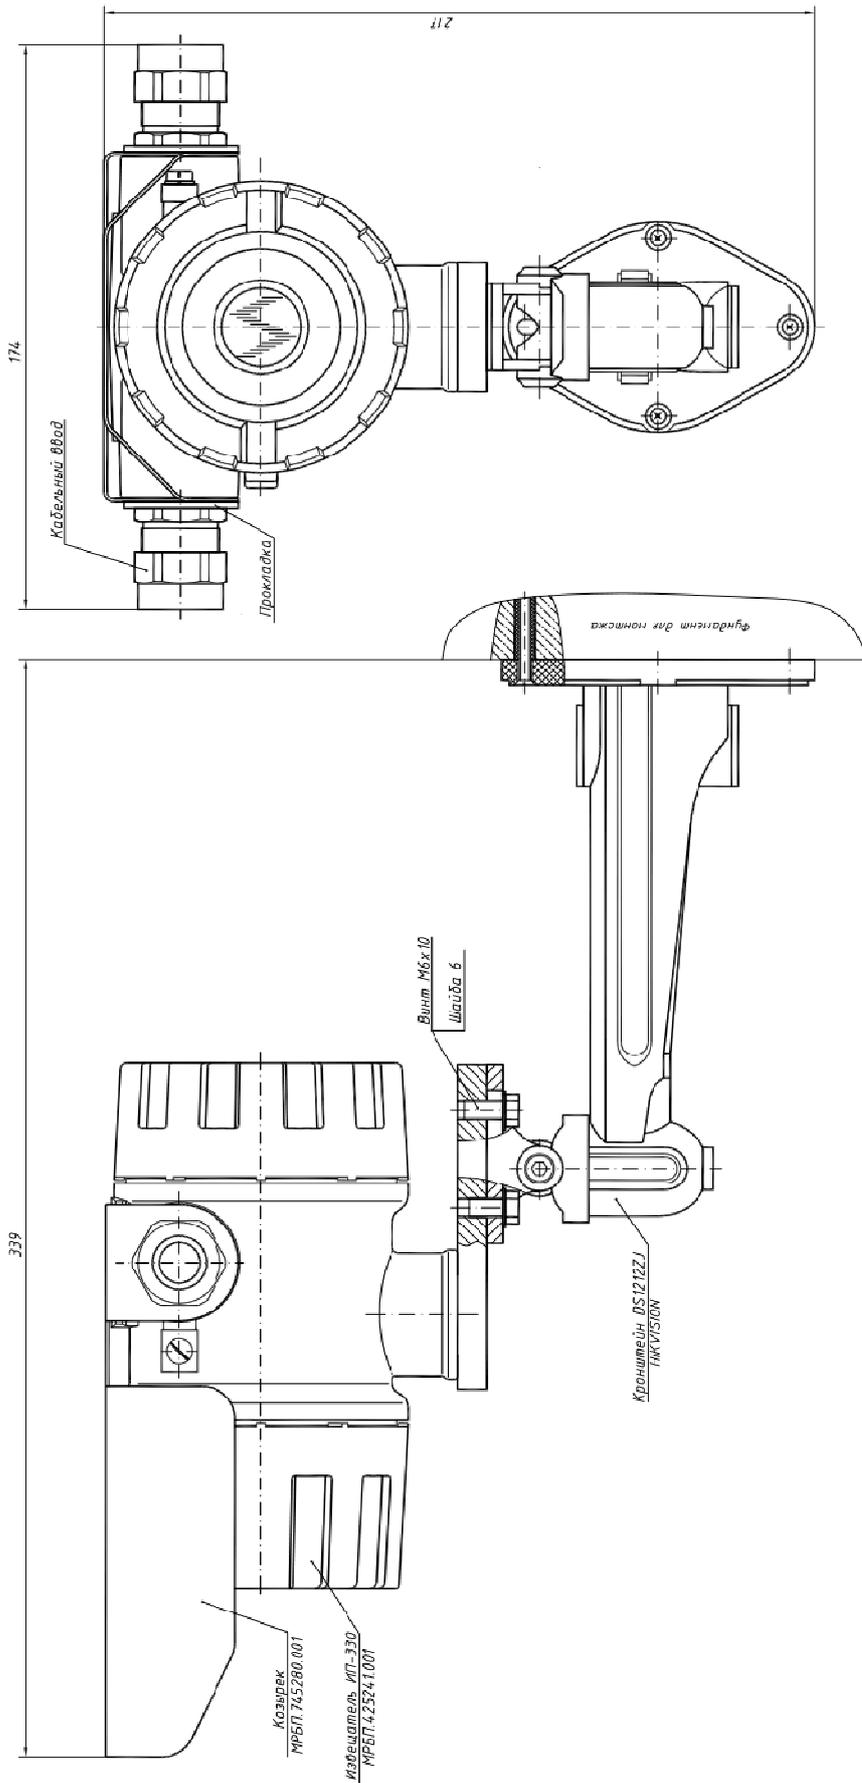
Габаритный чертеж ЭРИС ИП-330
